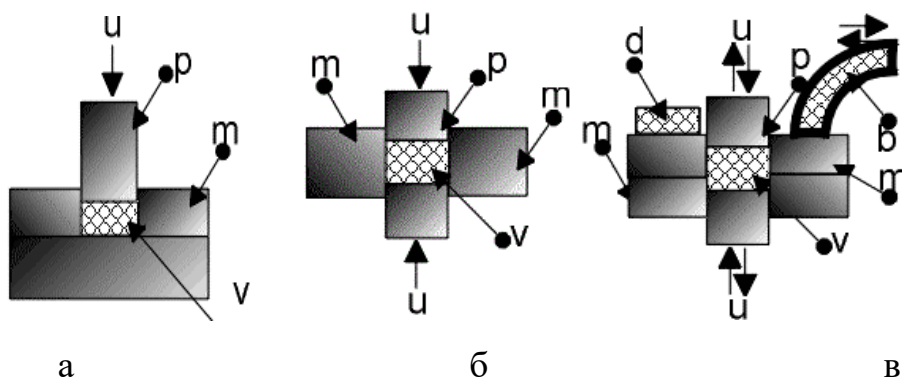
Различные варианты прессования: а – прессование с одним пуансоном; б – прессование с двумя пуансонами; в – прессование с автоматическим заполнением пресс-формы и выталкиванием готовой прессовки (u – направление усилия, m – матрица пресс формы, p – пуансон, v –прессуемое вещество (порошок), b - бункер-питатель, d – спрессованная деталь) [7]
